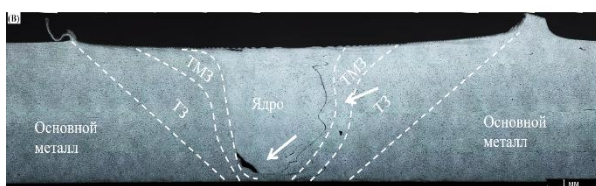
Комплексные дефекты в сварном соединении алюминийевого сплава АМг5, поперечное сечение, оптическая металлография, панорама
